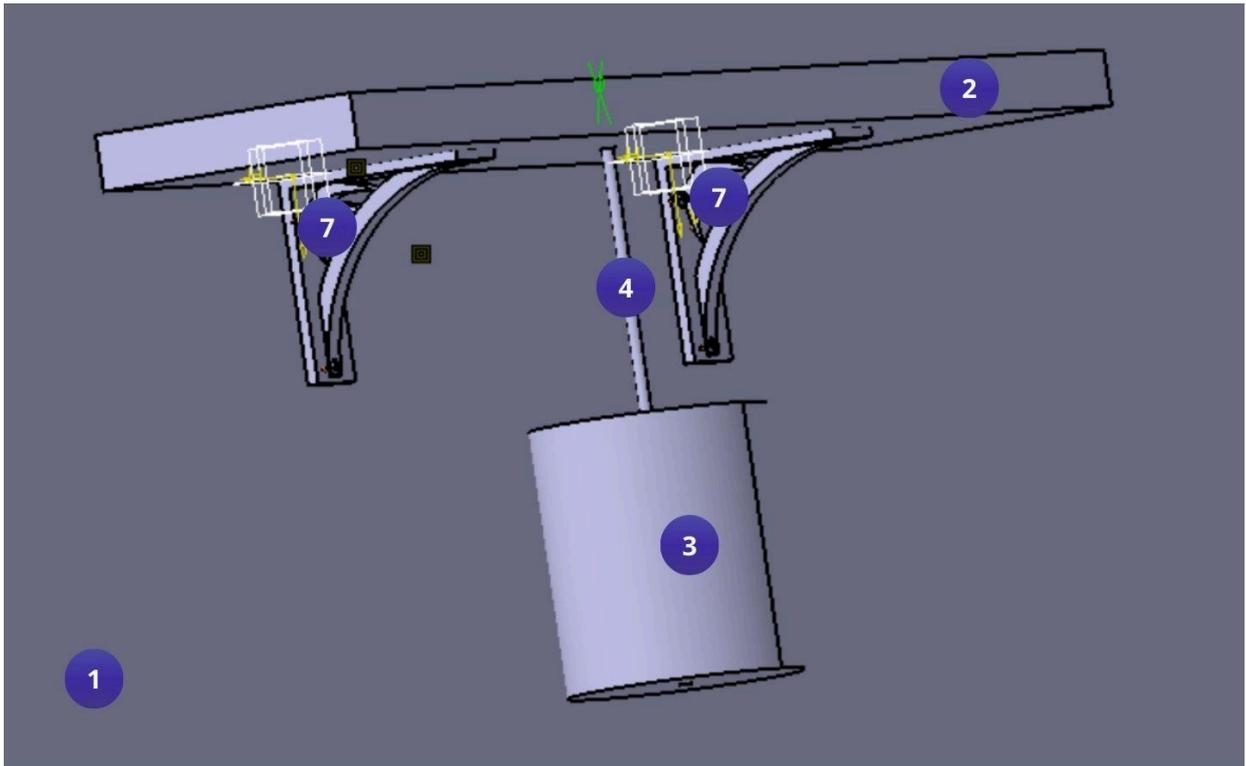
Illustration du montage complet de nos équerres au sein de l'assemblage
